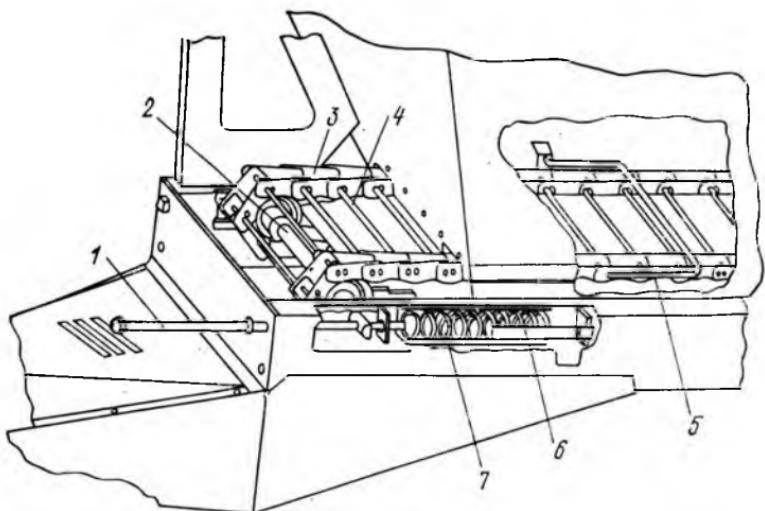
Механизм натяжения транспортера и приспособление для разгрузки кузова разбрасывателя РУМ-8:
